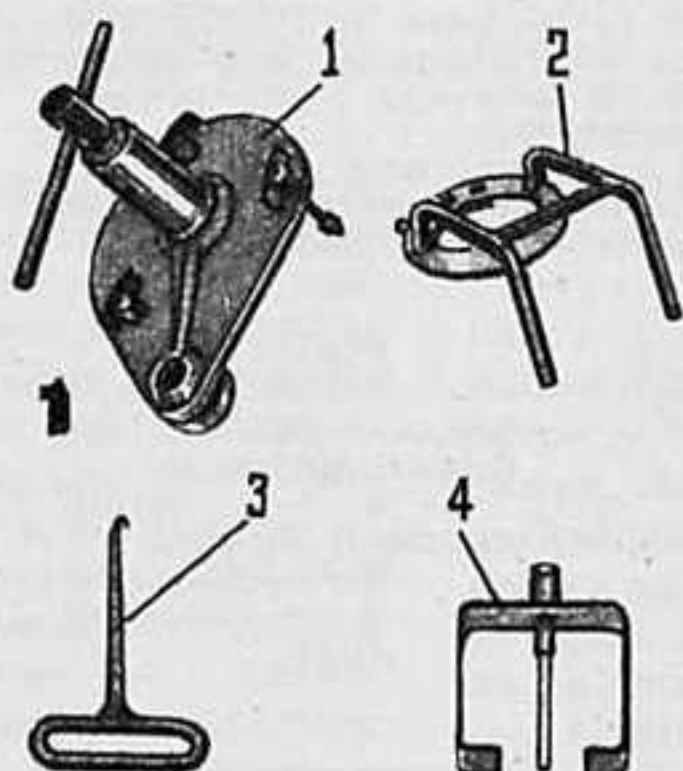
Приспособления: 1 — для разъединения половинок картера, извлечения и установки коленчатого вала; 2 — для разборки и сборки сцепления; 3 — крючок для разборки и сборки сцепления (его можно изготовить из спицы); 4 — съемник для ведущей звездочки передней передачи и ротора генератора.
